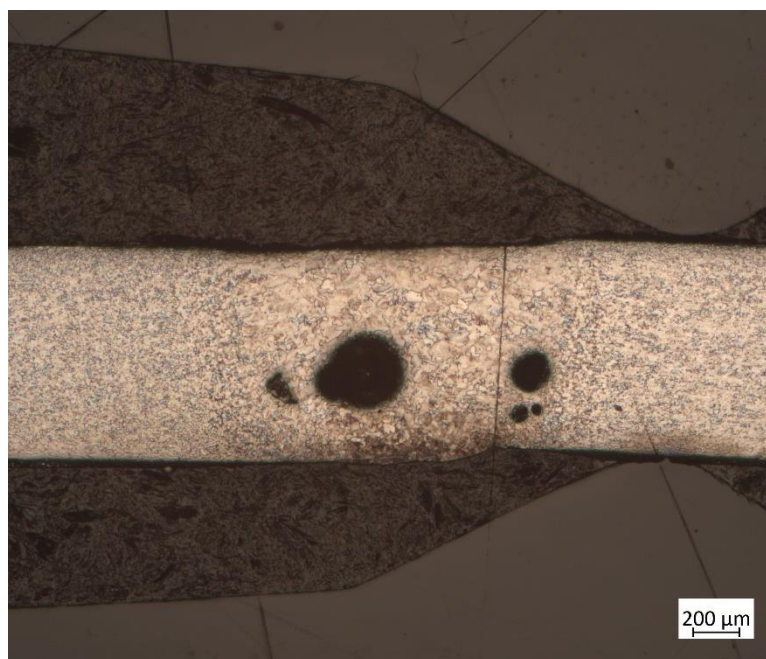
Vzorek 1 – před exploatací korozním testem – koutově přeplátovaný svar
